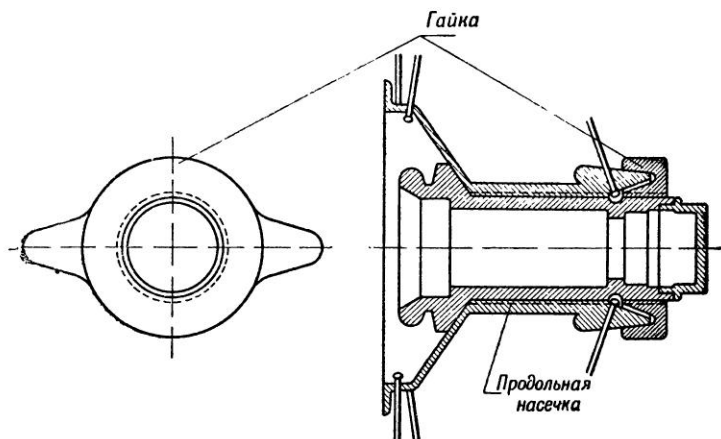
Легкосъемная втулка для крепления колес гоночного автомобиля
